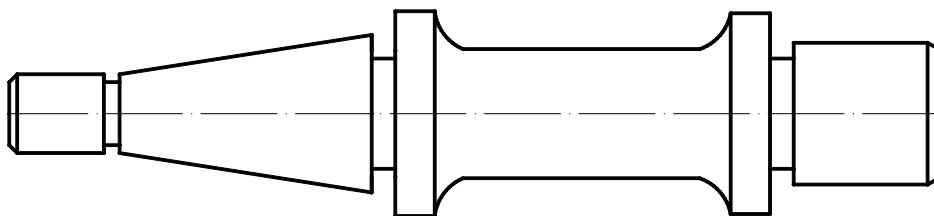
Przyłączanie kolejnych segmentów wałka (A i B – symetria boków)
